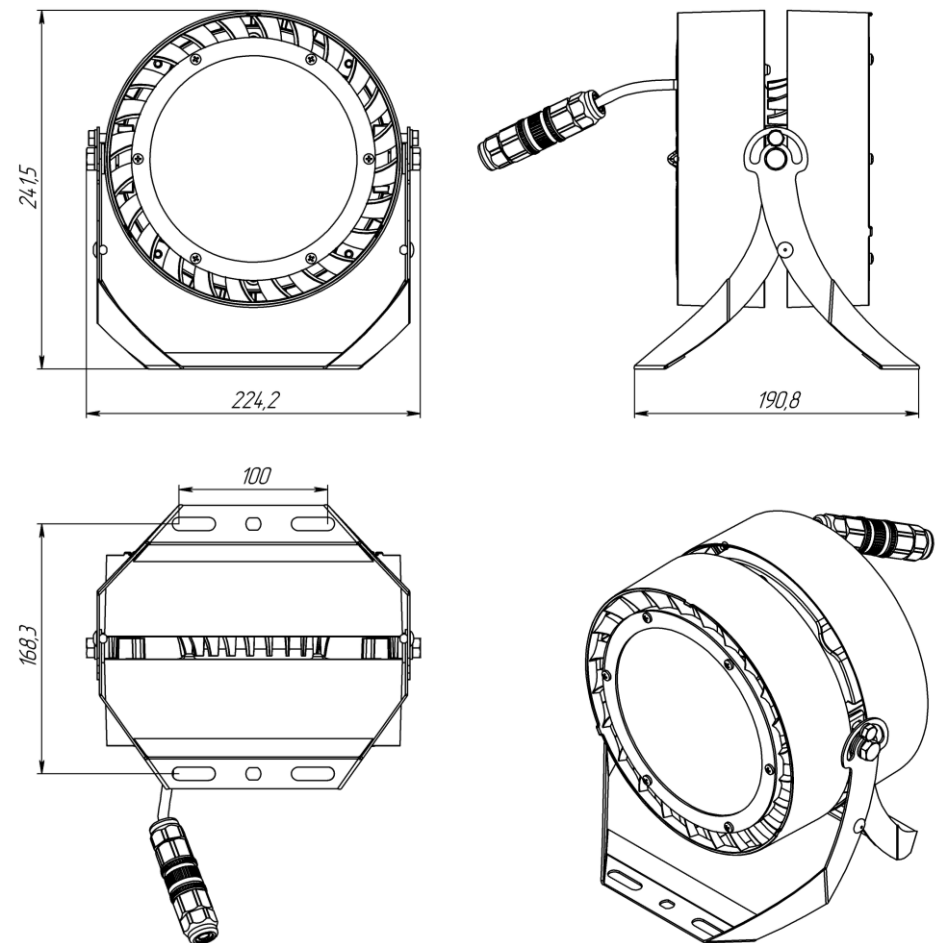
Общий вид светильника L-industry II banner с подвесным креплением.
